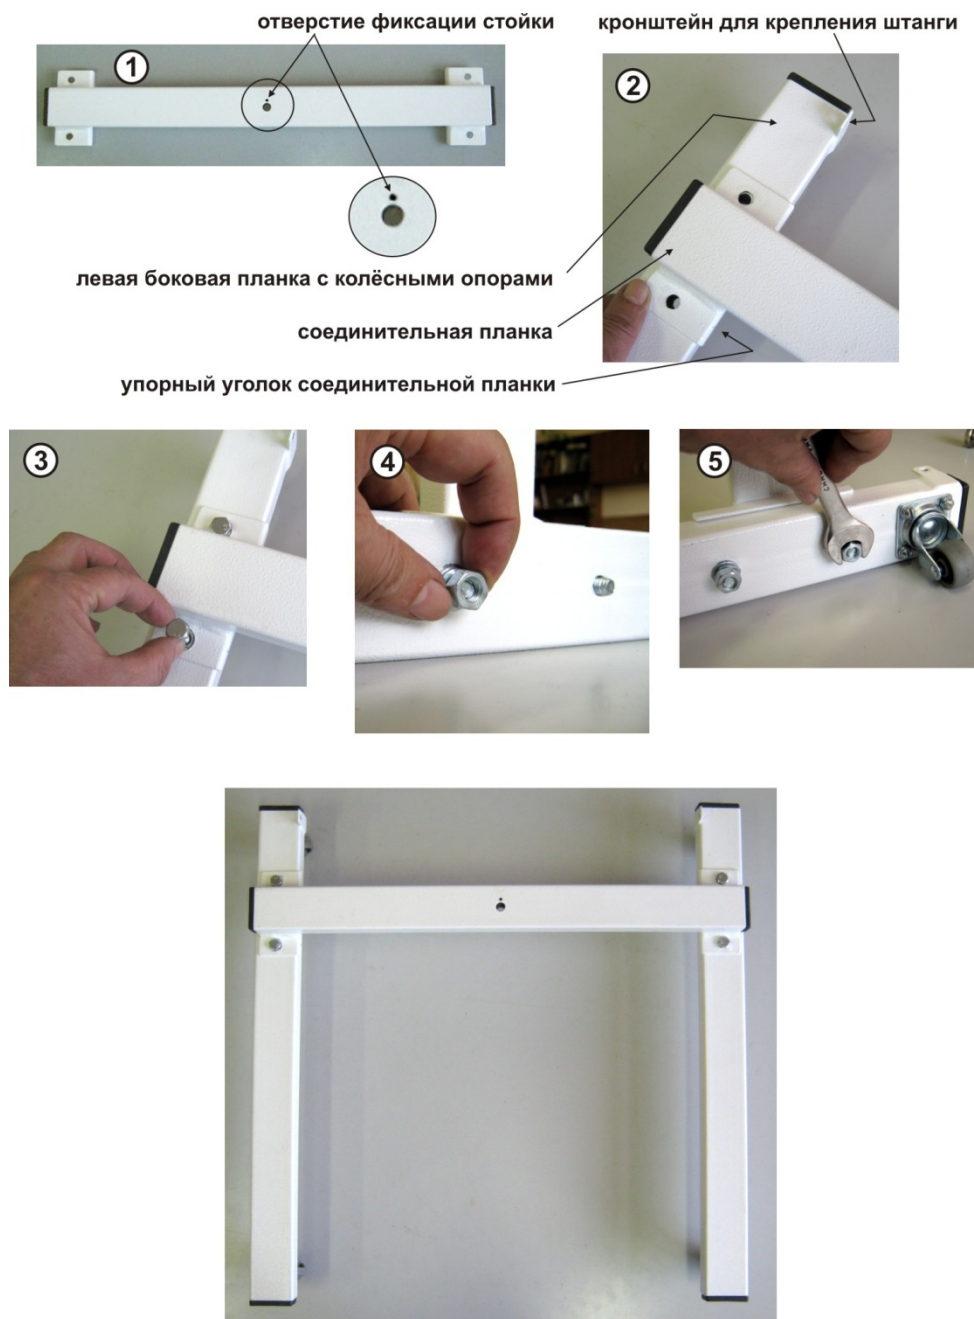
Соединение боковых планок (с колёсными опорами) с соединительной планкой основания.
